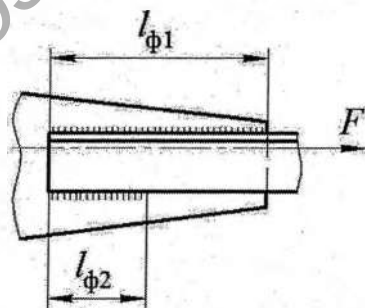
Сварное соединение косынки и углового профиля
